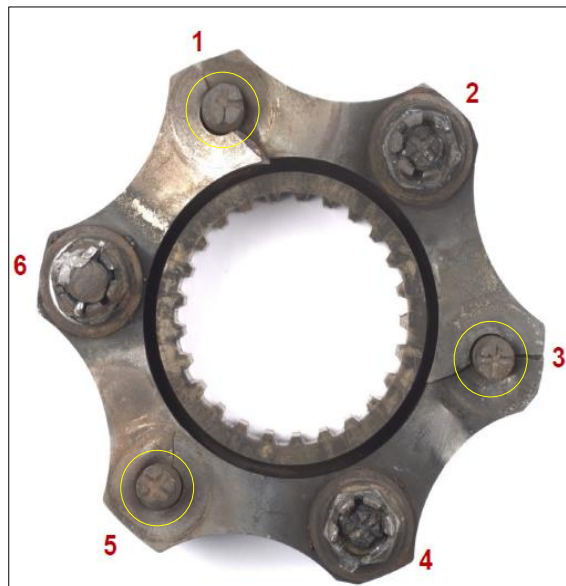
y 37: Vistas del Engine Shaft Flange.
